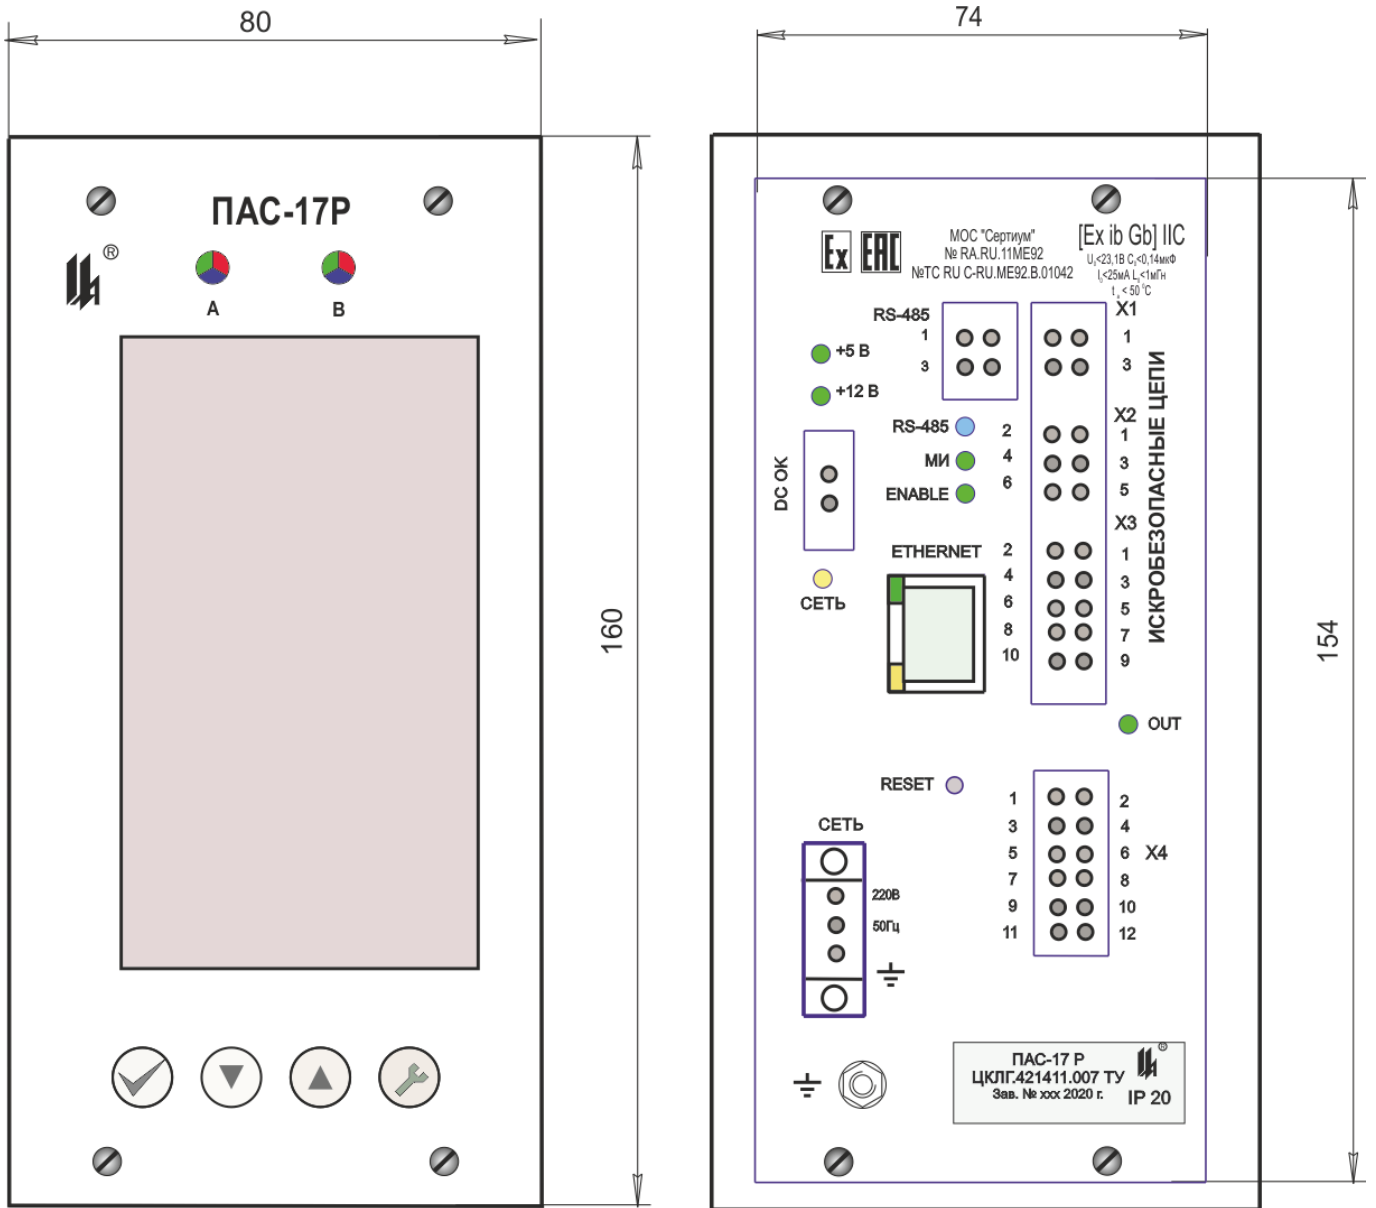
Внешний вид и габаритные размеры ПАС-17Р
